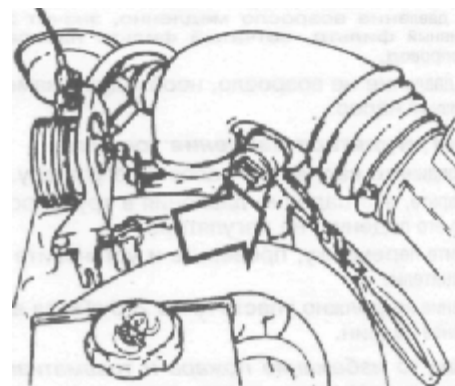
Перекрытие шланга воздушного клапана модель 960
